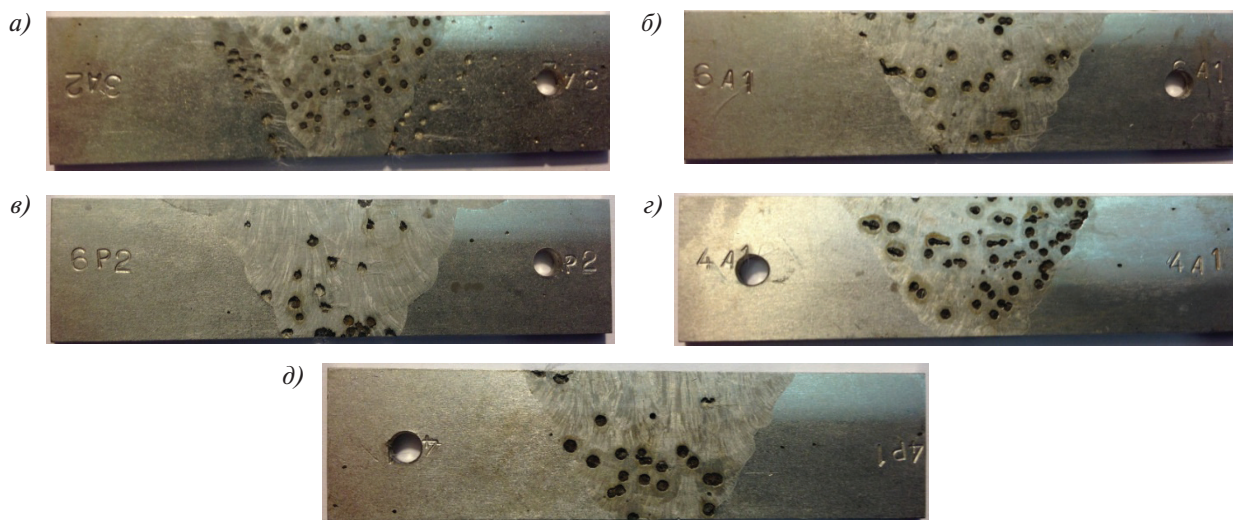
Распределение питтингов на поверхности образцов из сварных соединений стали X16H11M3, выполненных ручной аргонодуговой сваркой неплавящимся электродом с присадочной проволокой марки Св-04X17H10M2 (а, б, в) и ручной дуговой сваркой покрытыми электродами марки 48А-1 (в, д): а – плавка с 0,08С+0,01N; б – плавка с 0,06С+0,06N; в – плавка с 0,06С+0,06N; г – плавка с 0,02С+0,06N; д – плавка с 0,02С+0,06N
